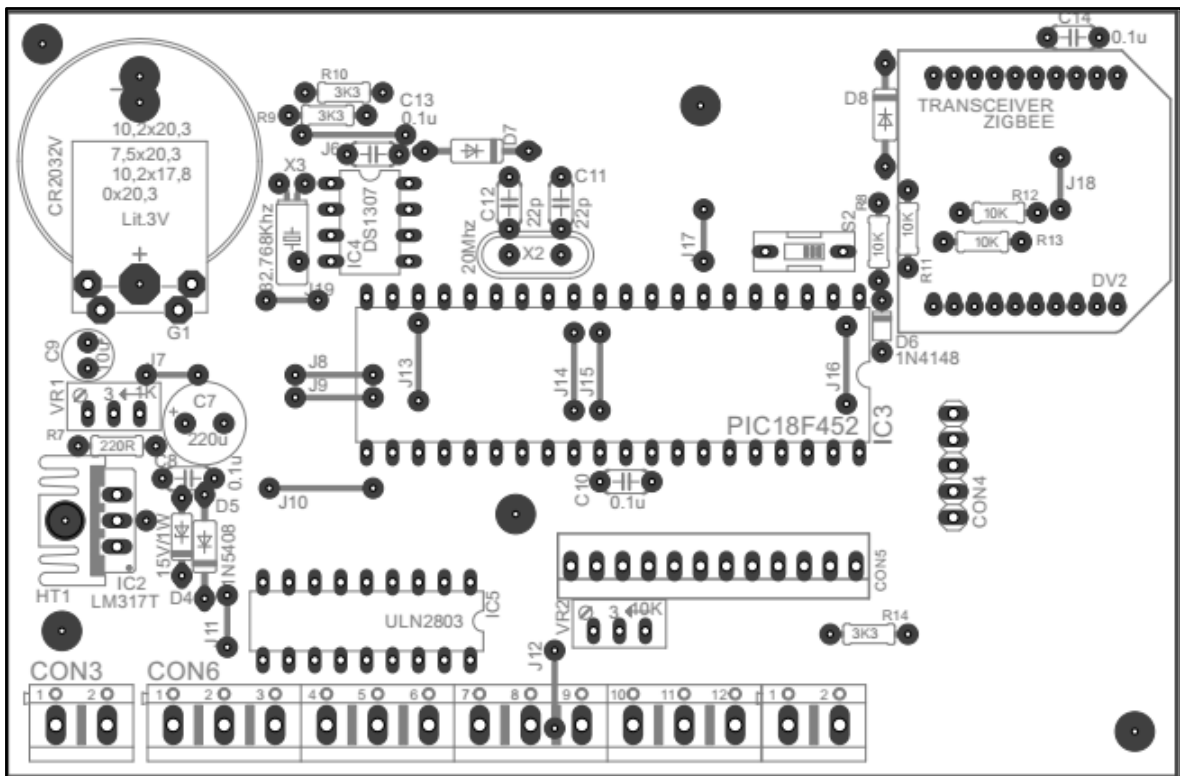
Elementos que componen el dispositivo principal. Fuente: La Autora.
